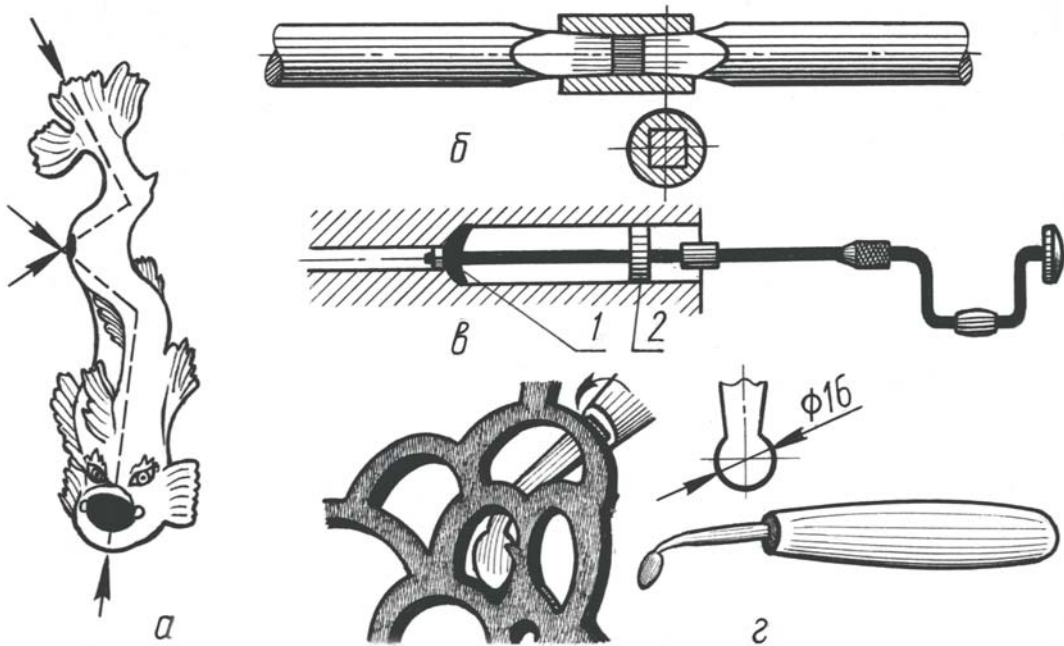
Изготовление полости в скульптуре рыбы и обработка её поверхности: а – направление удлинённого сверла; б – при сверлении исходного отверстия; в – расширение канала фрезы (1) с помощью коловорота и подшипника (2); г – резец с загнутым плоским кружком (пяточковый резец) для зачистки внутренней стороны стенок прорезей чешуи (см. рис. 180)
